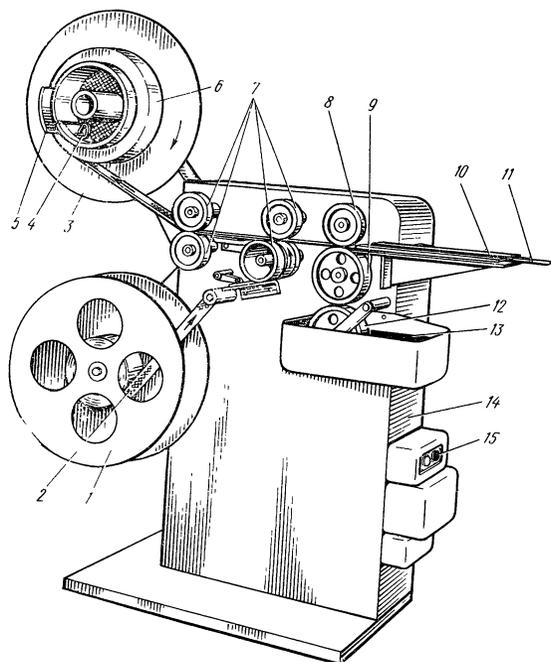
Станок для изготовления концевой изоляции («бортика»):
